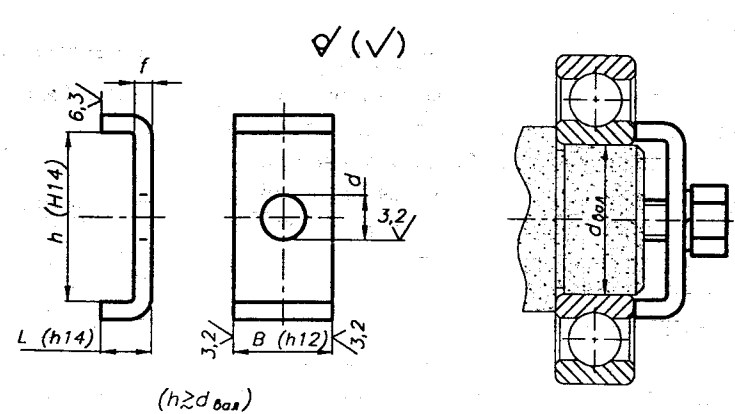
Конструкция и размеры стопорных скоб
